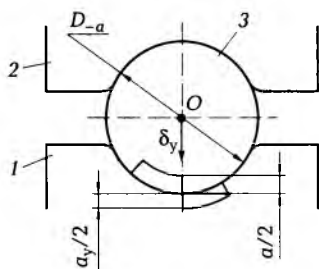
Схема установки базы «вал» в полуцилиндрические гнезда:
